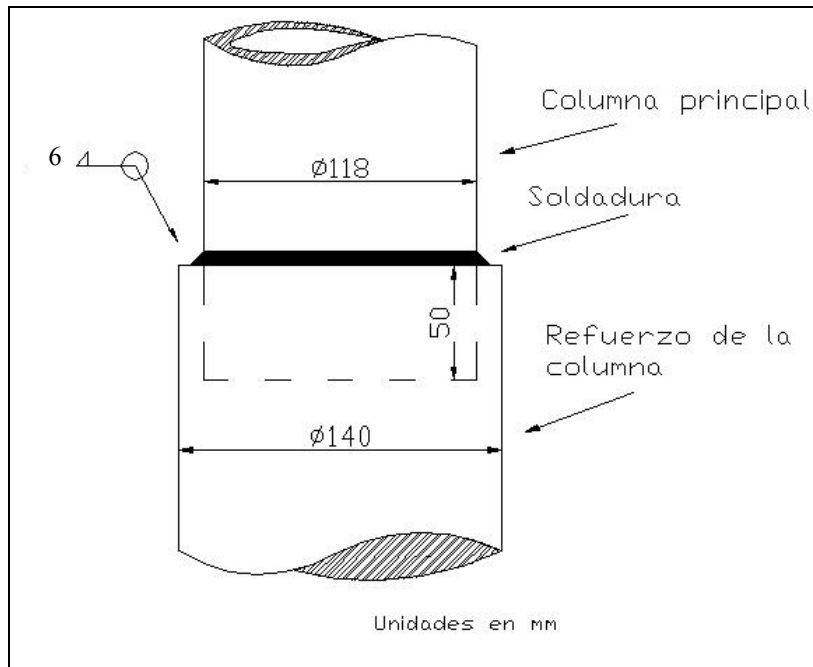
46. Soldadura del refuerzo y la columna principal. Fuente los autores.
